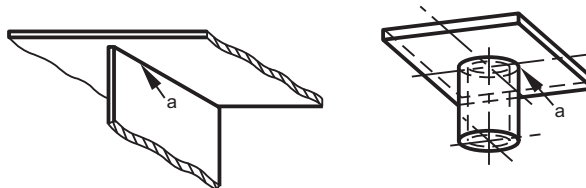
Exemples de positions principales de soudage (suite)
